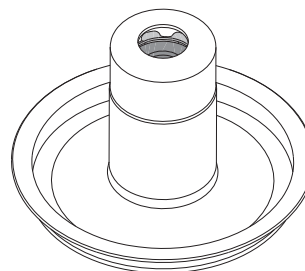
Корпус ротора с держателем подшипника и керамической втулкой подшипника
